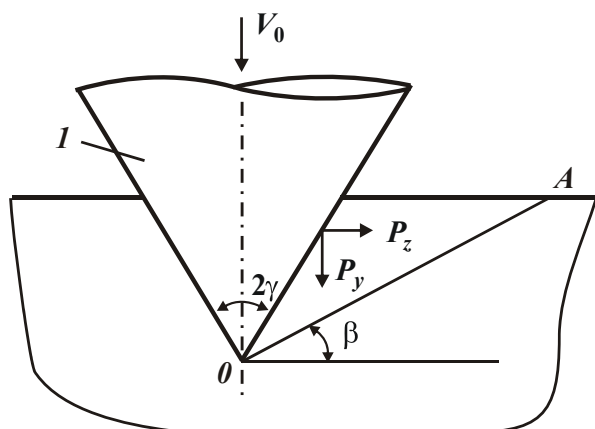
Розрахункова схема параметрів обробки для випадку $\alpha = 90^\circ$: 1 – зерно у формі конуса
